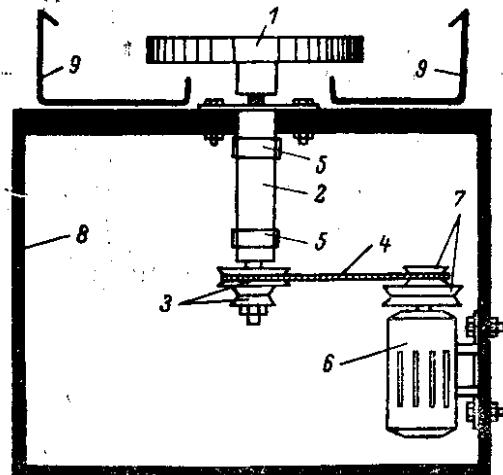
Планшайба горизонтальная (шлифовальный станок).
